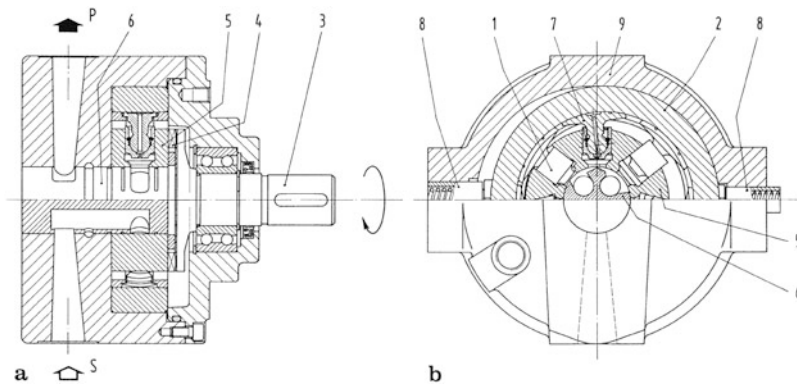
Radialkolbenpumpe, außen beaufschlagt (RKP, Moog). a Längsschnitt; b Querschnitt
